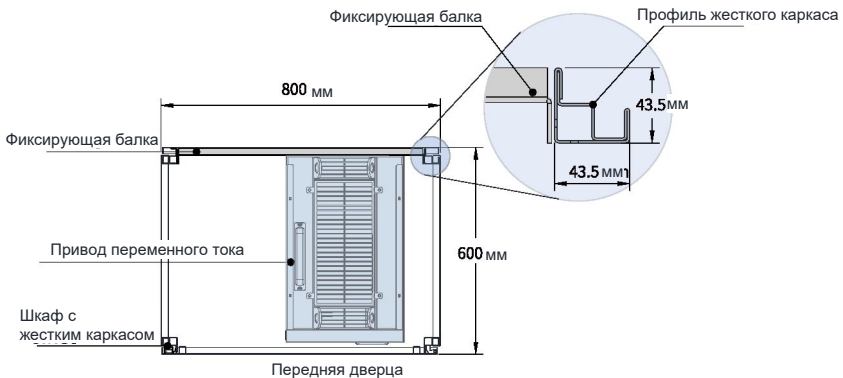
Вид шкафа сверху для моделей T11 и T12
